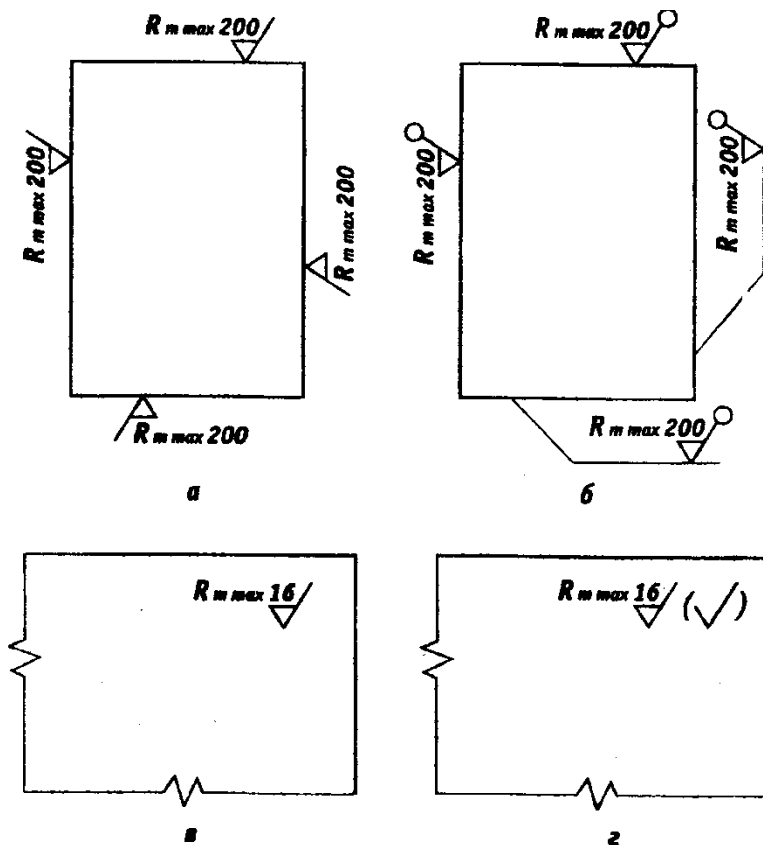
Обозначение шероховатости поверхностей: а – знак не имеет полку; б – знак имеет полку; в – одинаковая шероховатость поверхностей; г – шероховатость остальных поверхностей.
